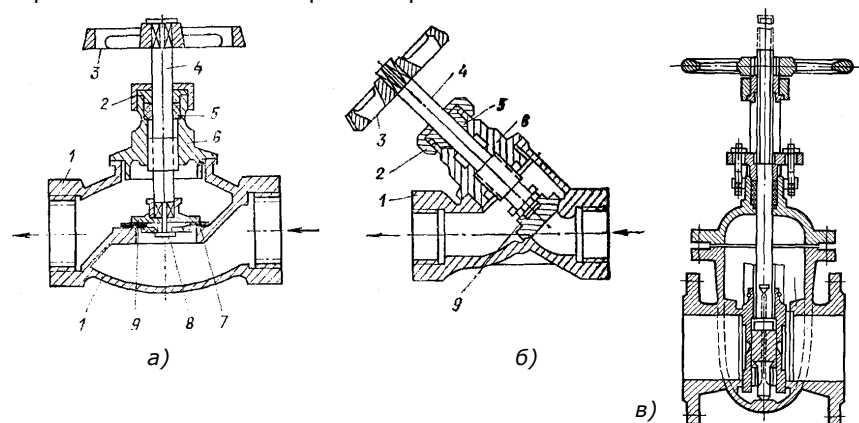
Запорная арматура: а – вентили прямой и косой; б) – задвижка проходная; в) – задвижка шлюзовая; 1 – корпус; 2 – накидная гайка; 3 – маховик; 4 – шпindel; 5 – сальник; 6 – головка; 7 – резиновая прокладка; 8 – винт и шайба; 9 – клапан в сборе
